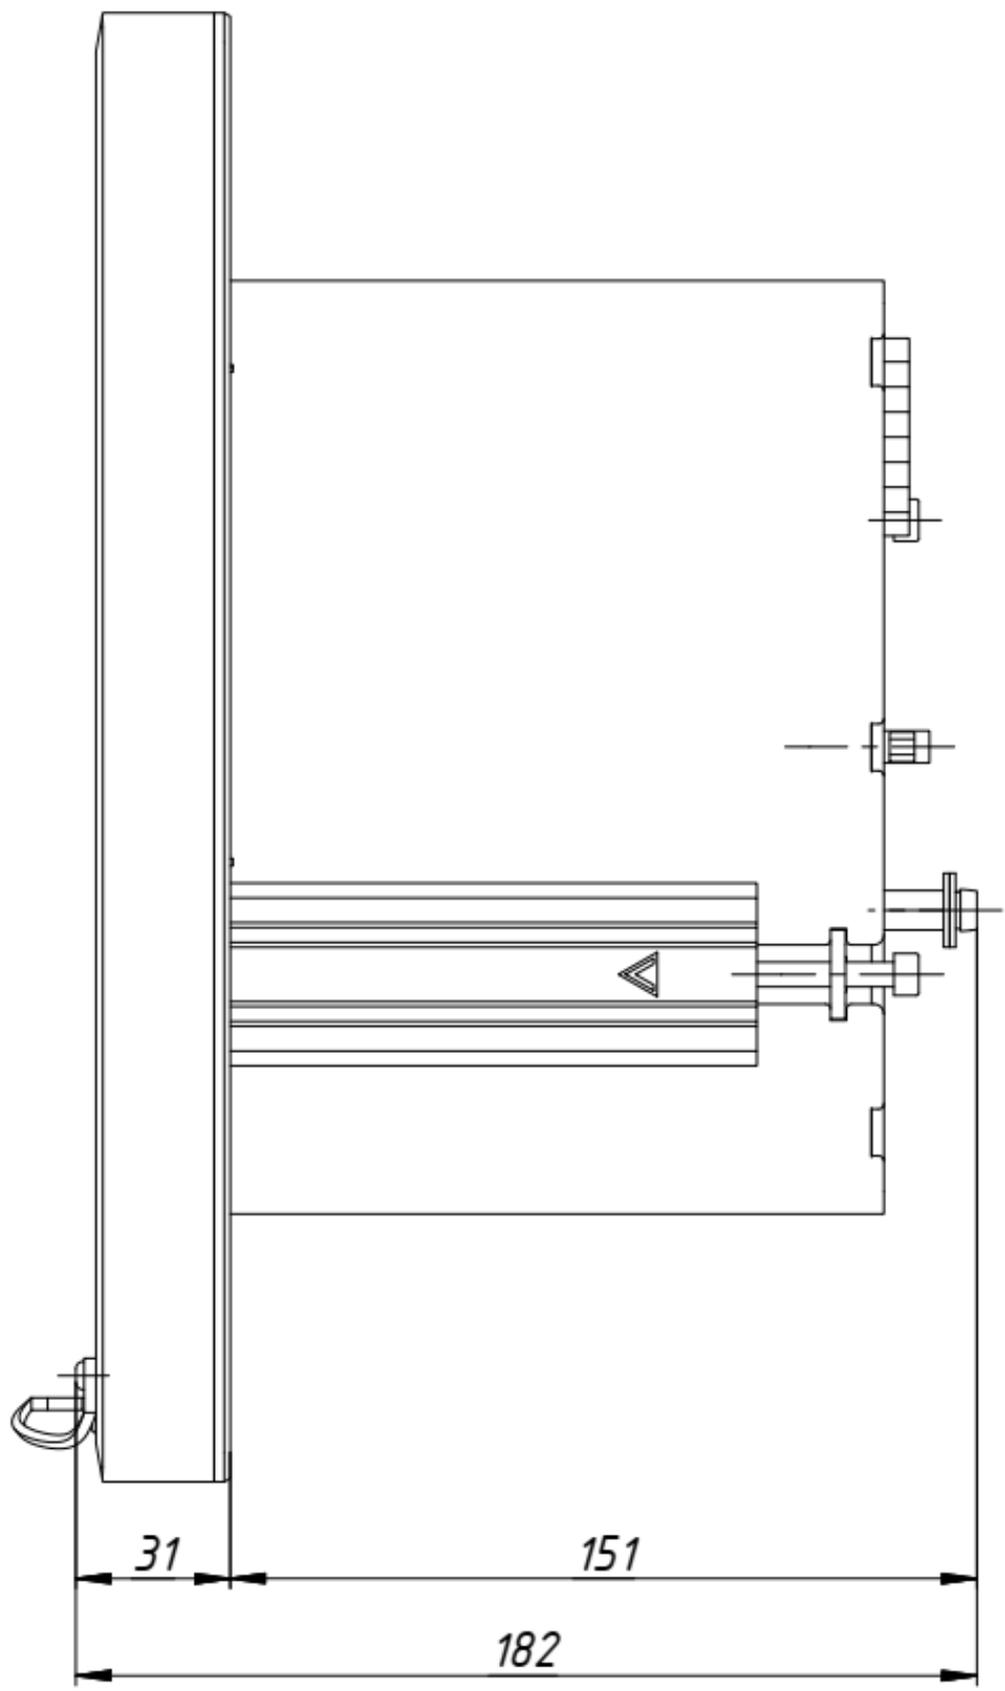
Габаритный чертёж прибора в исполнении Ф1772–3, вид сбоку
